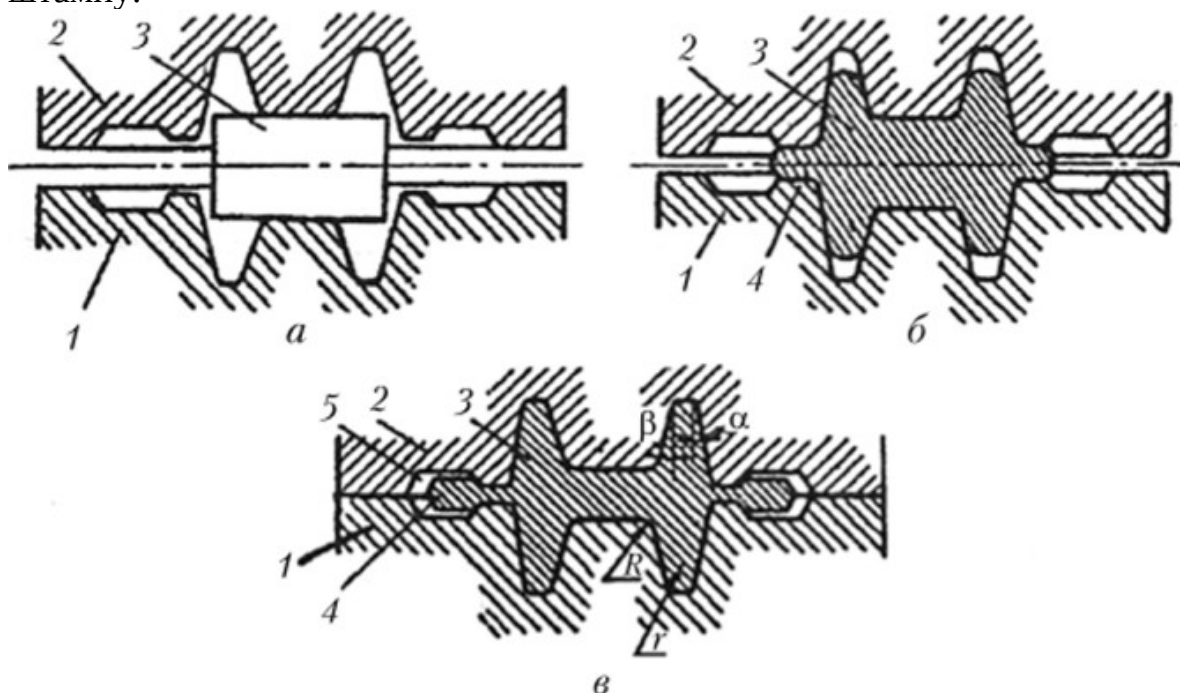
а - початкова стадія; б - стадія освіти задирки; в - кінцева стадія штампування; 1,2 - нижня і верхня половини штампа; 3 - вихідна заготовка; 4 - задирок; 5 - заусенечная канавка
